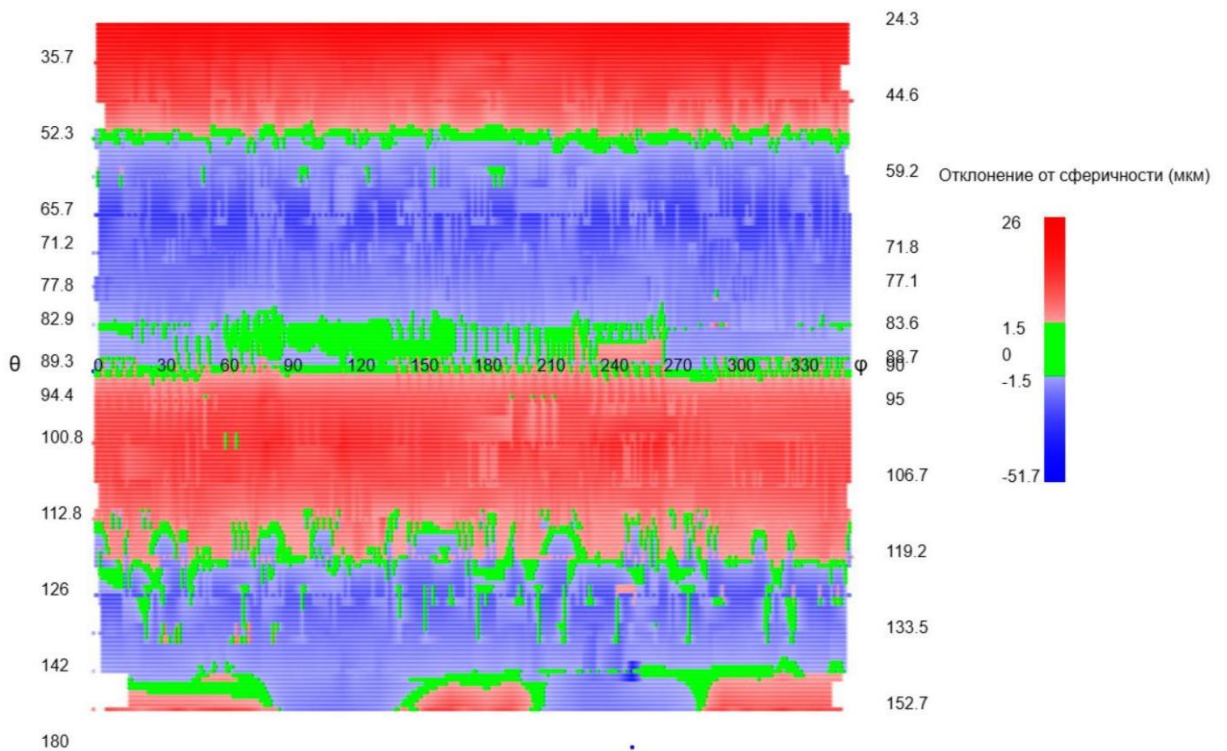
Развертка сферической поверхности шарового пальца №1 после притирки
